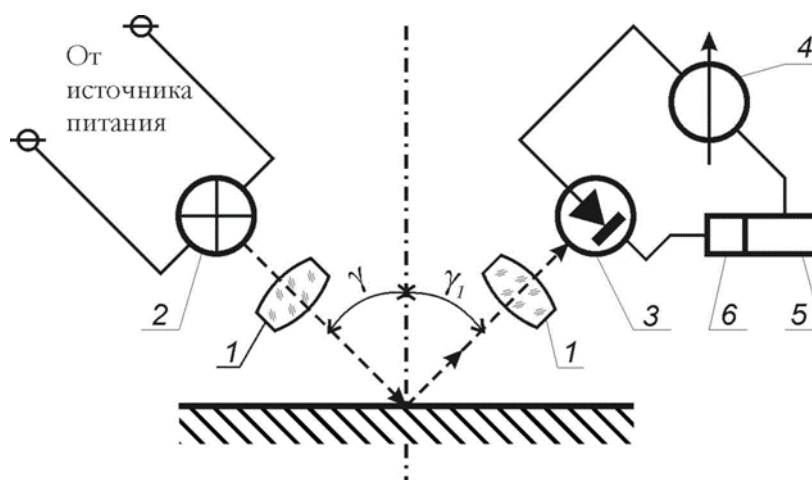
Фотоэлектрический датчик контроля блеска поверхности
